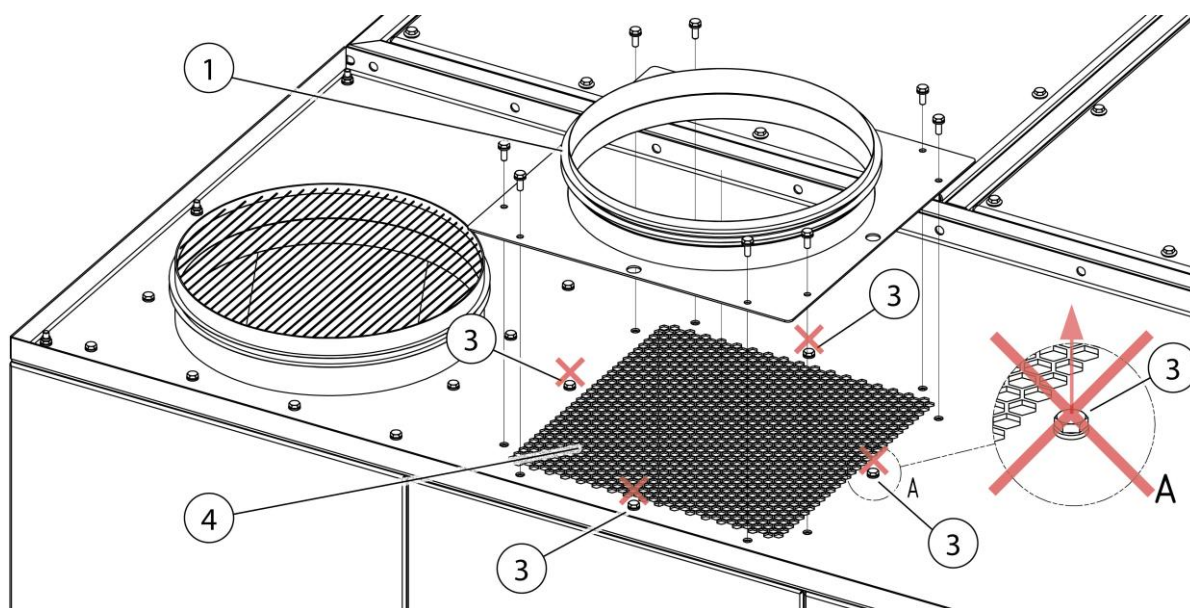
Montage de la tubulure de raccordement sur le produit
